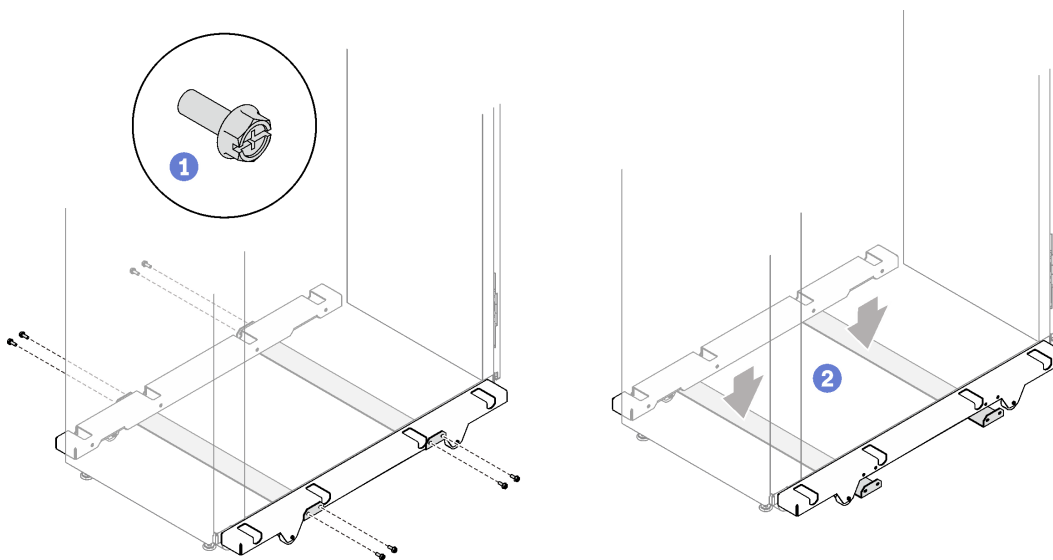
Rimozione delle barre stabilizzatrici degli stabilizzatori
